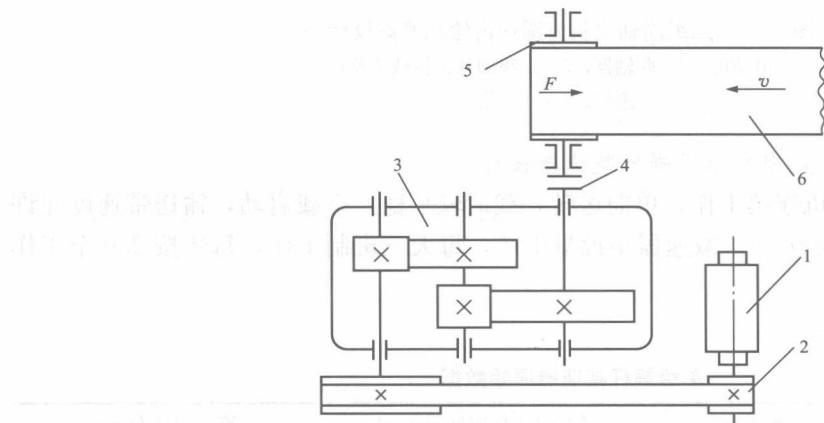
二级展开式直齿圆柱齿轮减速器设计
